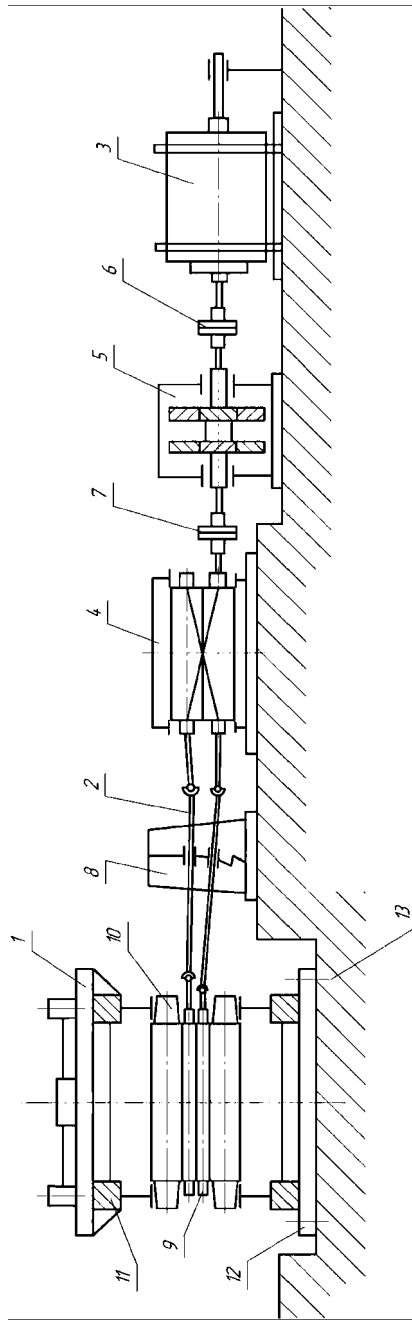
Главная линия рабочей клетки: 1 – рабочая клетка; 2 – шпиндели; 3 – электродвигатель; 4 – шестеренная клетка; 5 – редуктор; 6 – моторная муфта; 7 – коренная зубчатая муфта; 8 – механизм уравновешивания; 9 – опорный валок; 10 – опорный валок; 11 – станна; 12 – плитовина; 13 – анкерные болты
